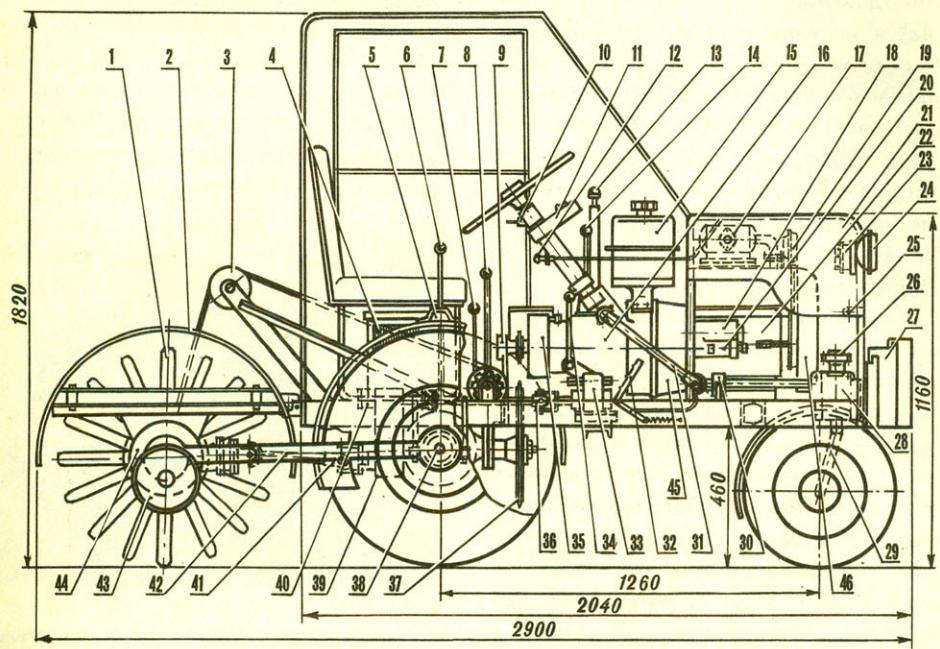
Мини-трактор конструкции Н. Хохлова с фрезой:
